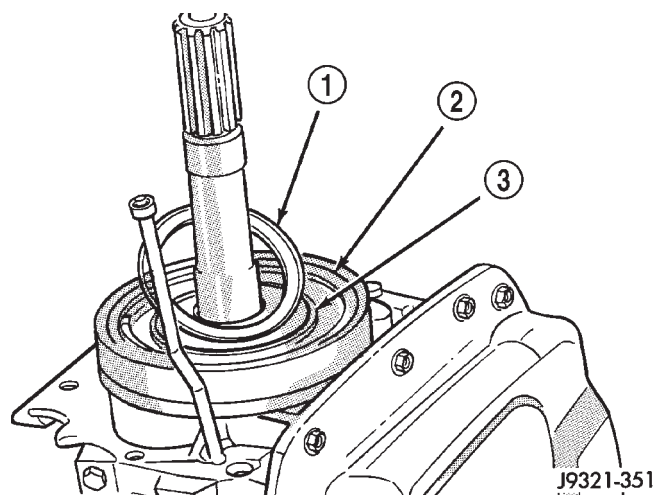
Desmontaje e instalación del cojinete de empuje del émbolo de sobremarcha
